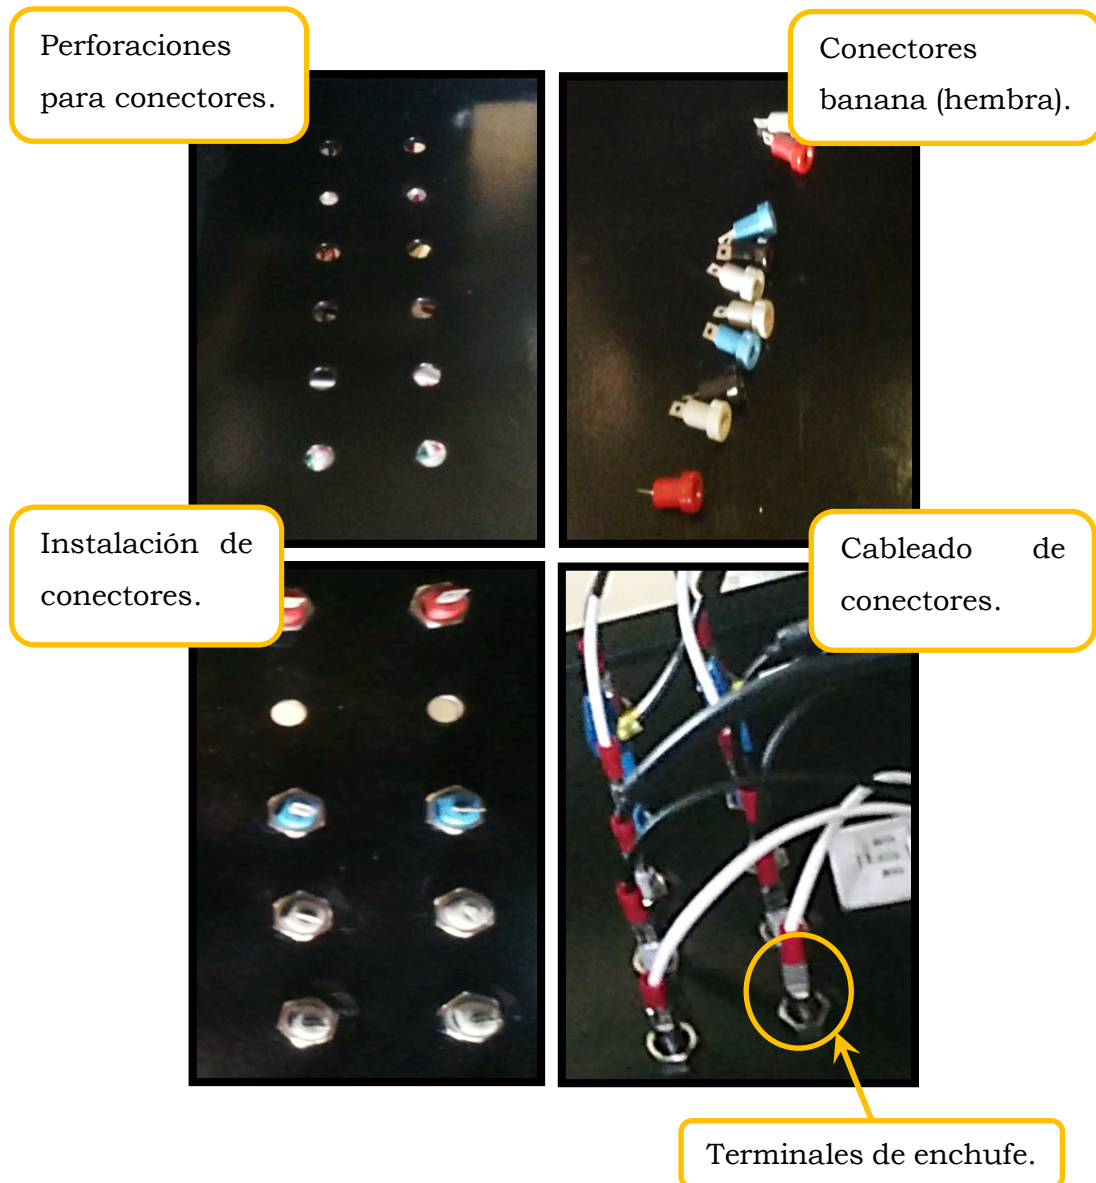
Montaje de conectores para salidas del módulo K60. Se puede observar la perforación de la estructura e instalación de los conectores hembra.
